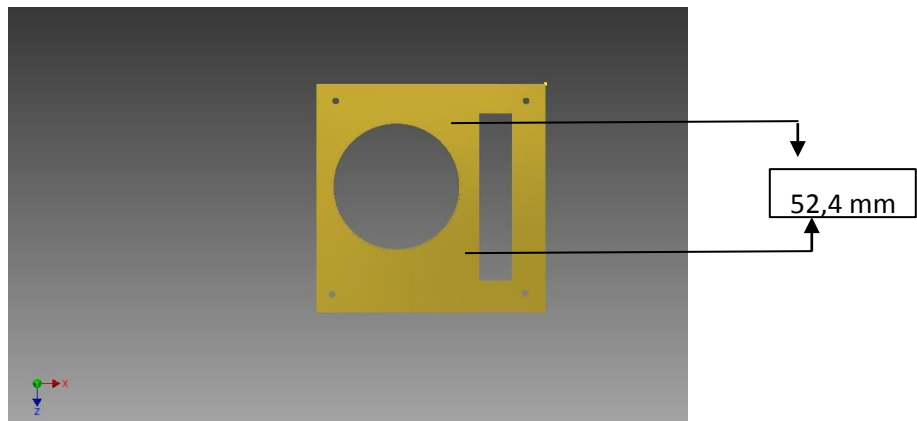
Sillinder dan piston 50mm tampak belakang
